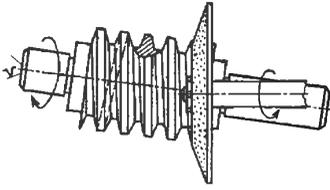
Схема шлифования червяка на резьбошлифовальном станке
